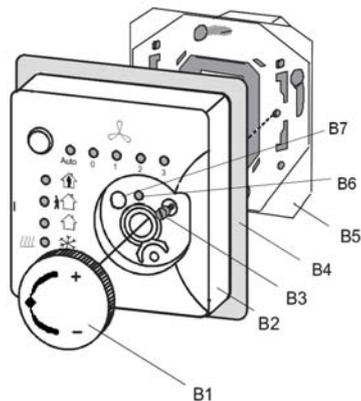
Montage des Fan-Coil Unit Bediengerätes
